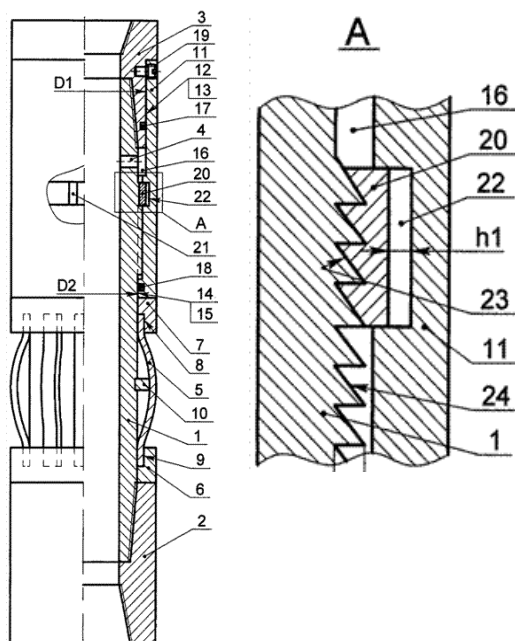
Центратор гидромеханический: 1 – корпус; 2, 3 – нижний и верхний переводники; 4 – радиальный канал; 5 – центрирующие элементы; 6, 7 – нижняя и верхняя втулки; 8, 9 – пазы; 10 – кольцо; 11 – дифференциальная втулка; 12, 14 – верхняя и нижняя расточки; 13, 15 – проточки; 16 – полость; 17, 18 – уплотнительные кольца; 19 – срезной штифт; 20 – упругодеформируемое кольцо; 21 – разрез; 22 – канавка; 23 – кольцевые канавки; 24 – выступ; А – узел фиксации центрирующих элементов в рабочем положении
